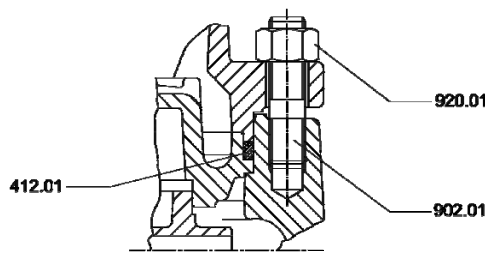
Типоразмеры для диаметра вала 24 на уплотнении вала
